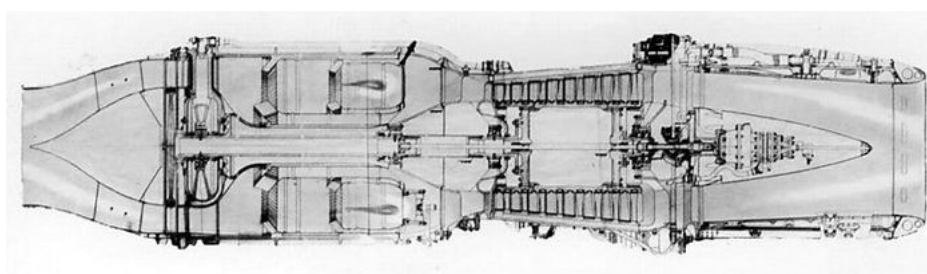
Řez německého proudového motoru Junkers Jumo 004 [14]
